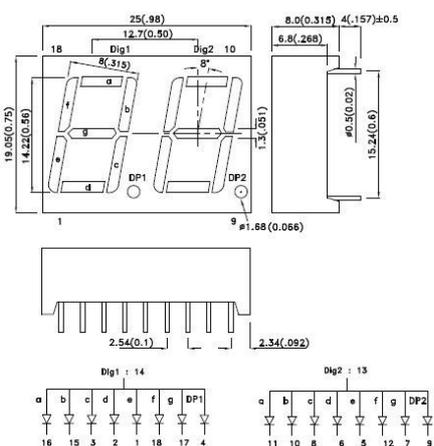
Размеры и внешний вид двойного семисегментного индикатора
